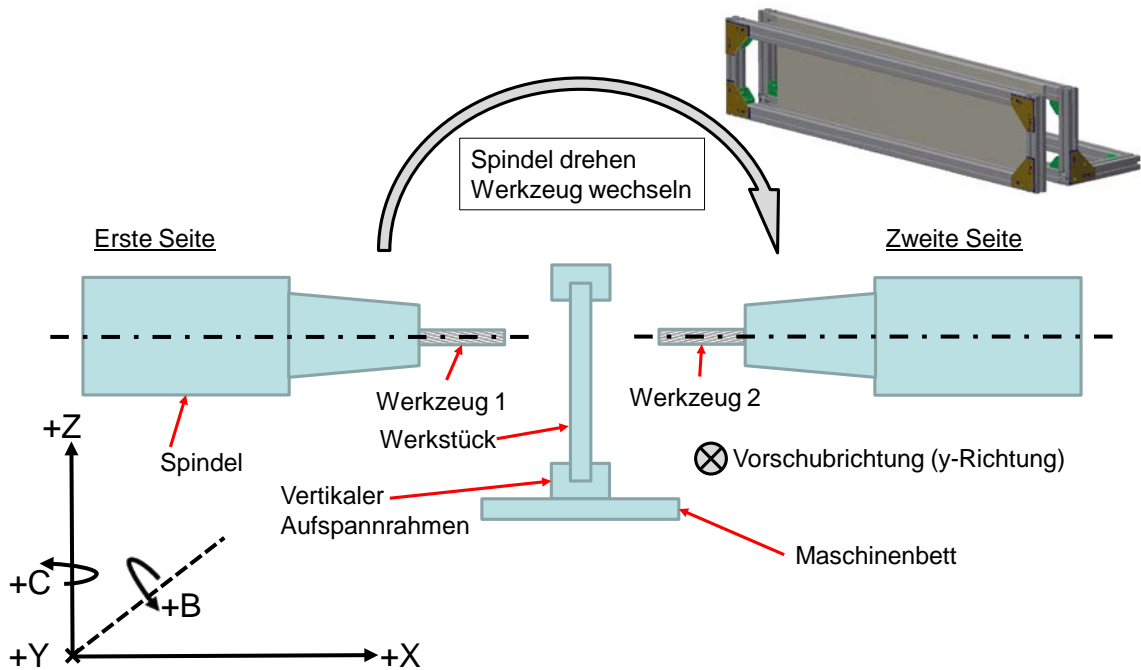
Werkzeugkonzepte zum beidseitigen Bearbeiten
